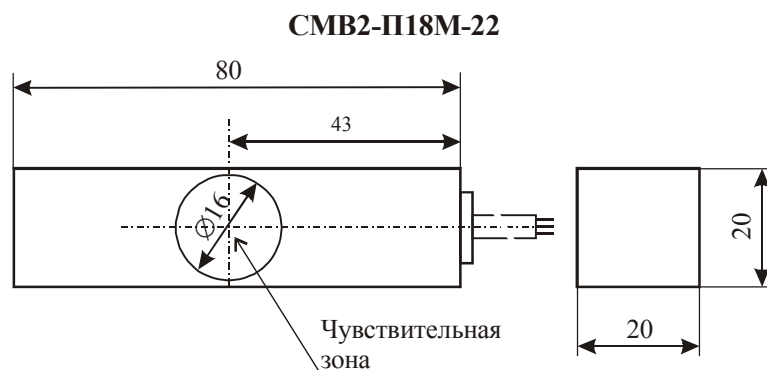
Внешний вид и габаритные размеры датчиков типа СМА2-П18М-22
